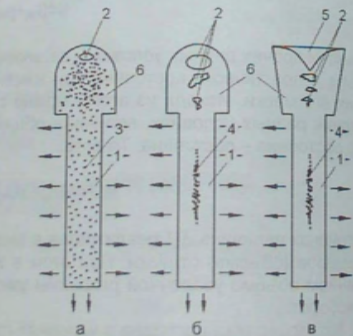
Схемы расположения усадочных дефектов в отливках, затвердевших в условиях преимущественного теплоотода от отливки: 1 – отливка; 2 – усадочная раковина закрытого типа; 3 – пористость распродоточенная; 4 – пористость сосредоточенная; 5 – усадочная раковина открытого типа; 6 – прибыль
